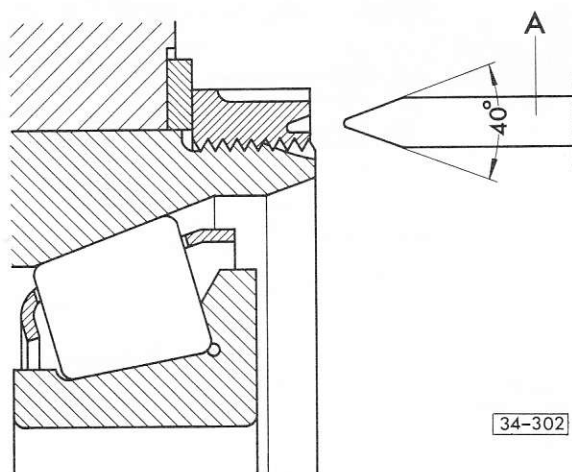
Ecrrou de serrage: matage en deux endroits pour le freiner
